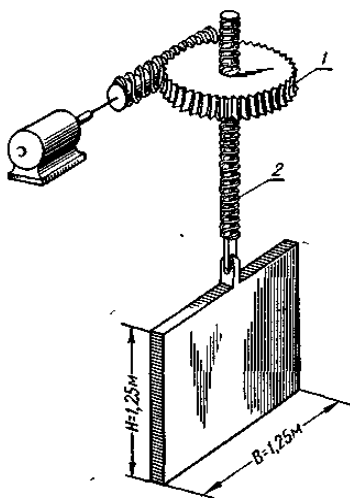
Кинематическая схема подъемного механизма с червячным редуктором: 1 – червячное колесо; 2 – грузовой винт
